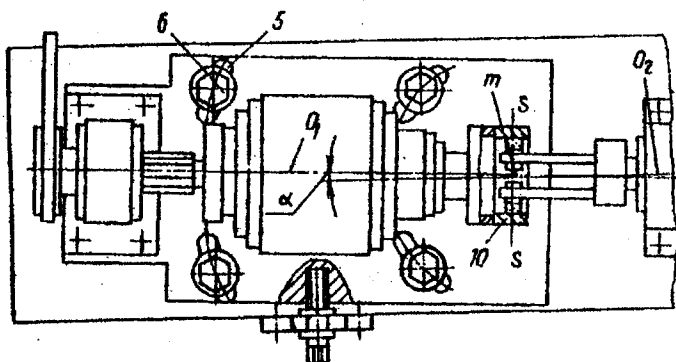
Конструкция станка типа КХВ (вид сверху)
